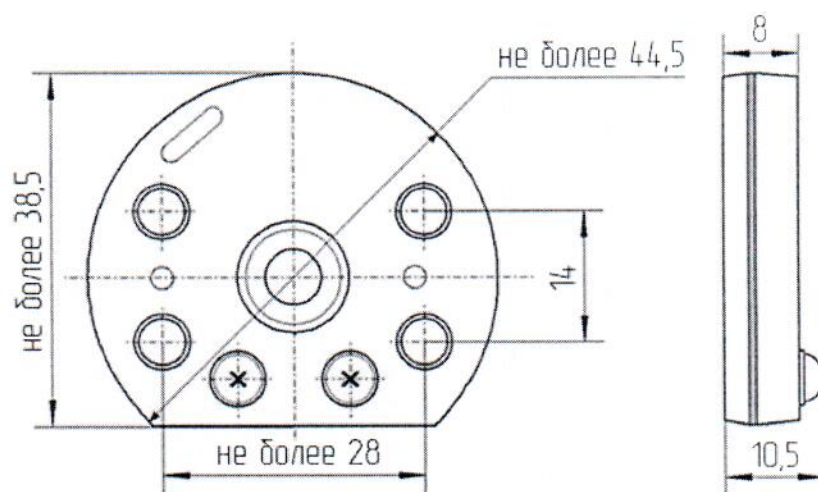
Преобразователь в корпусе Т для установки внутри клеммной головы ПП. Степень защиты оболочки IP20.
